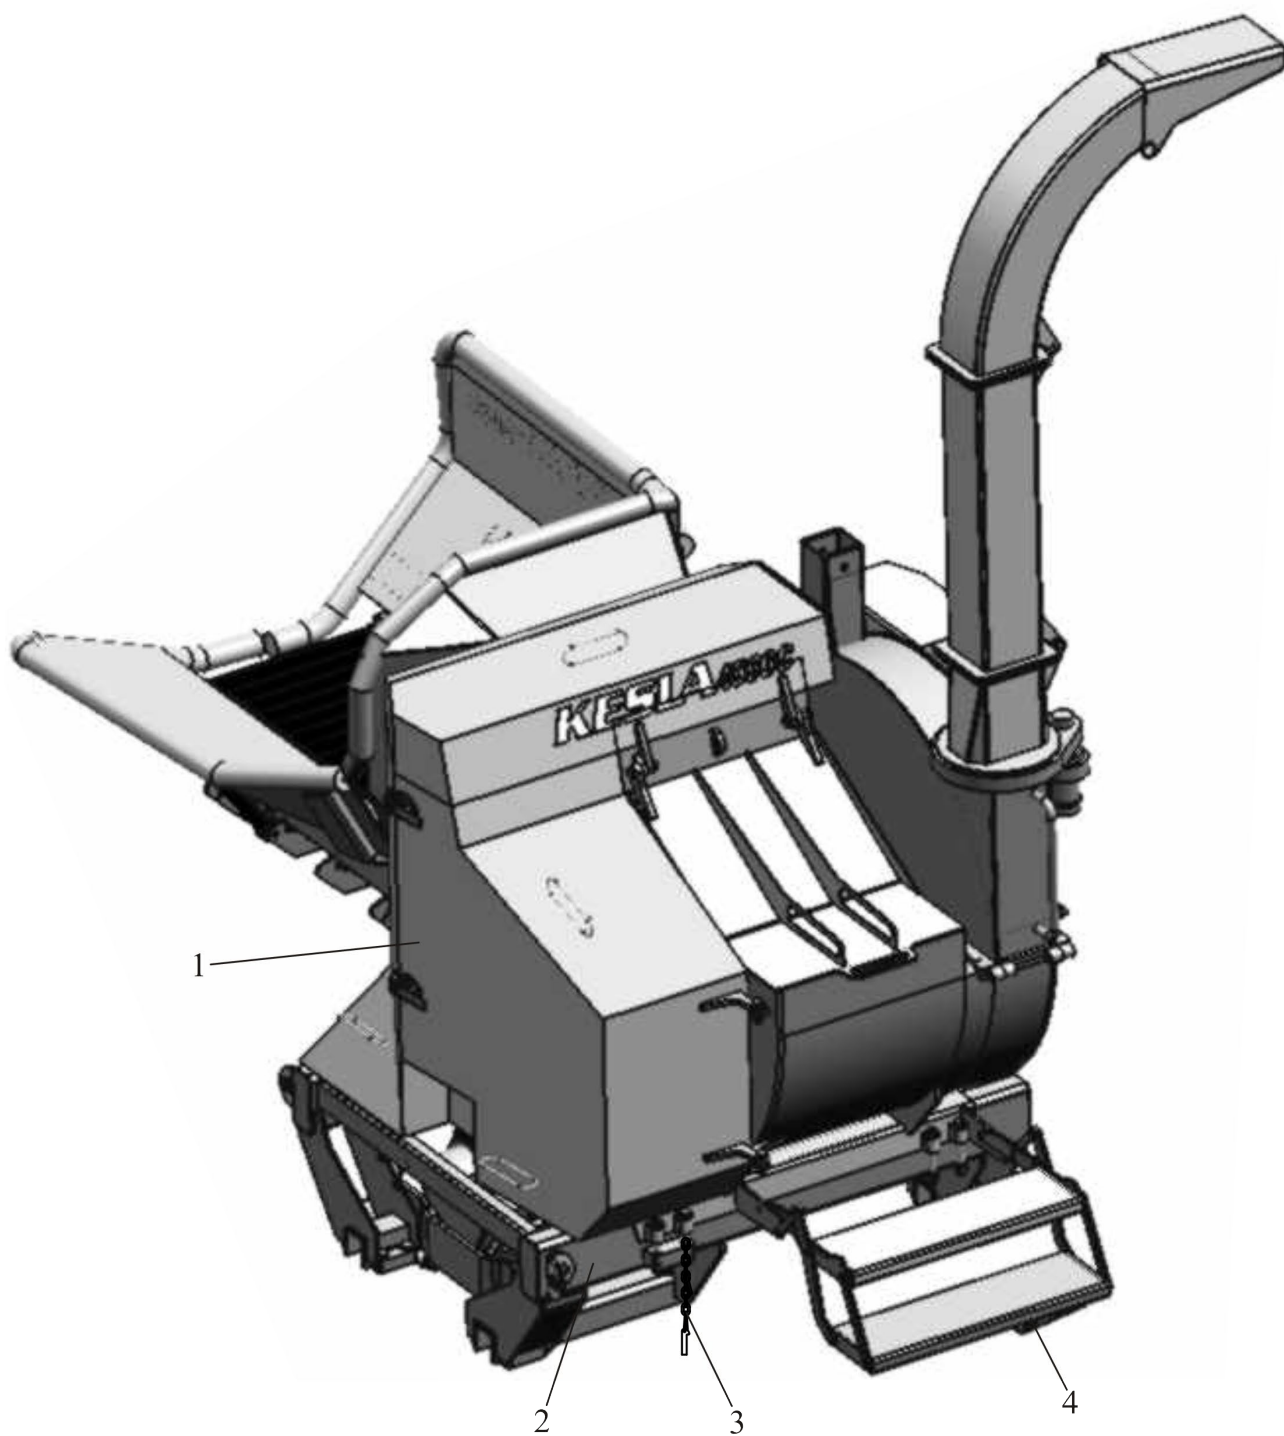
(лист 1 из 2) – Агрегат дробильный
